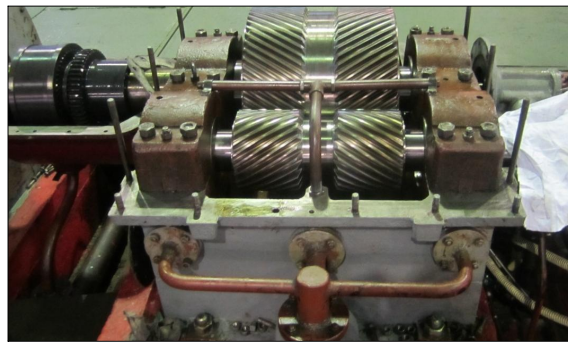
Редуктор РЦОТ 350-2,55-1К
